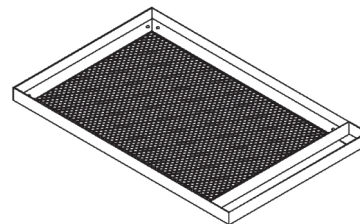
Disposición constructiva de las bandejas desarrolladas en este estudio.
